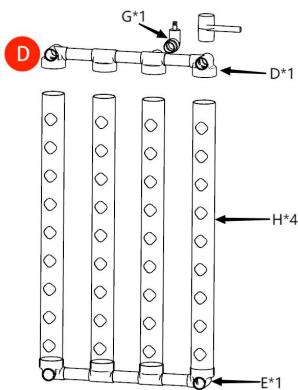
Conecte un conjunto de tubos compuestos conectores , cuatro tuberías de plantación, un conjunto de tuberías compuestas de salida de agua con la letra D y un grifo de salida según el diagrama, con las tuberías de plantación hacia arriba. Refuerzalos con un martillo de goma (golpea cada conexión con el martillo de goma hasta que encajen bien)
